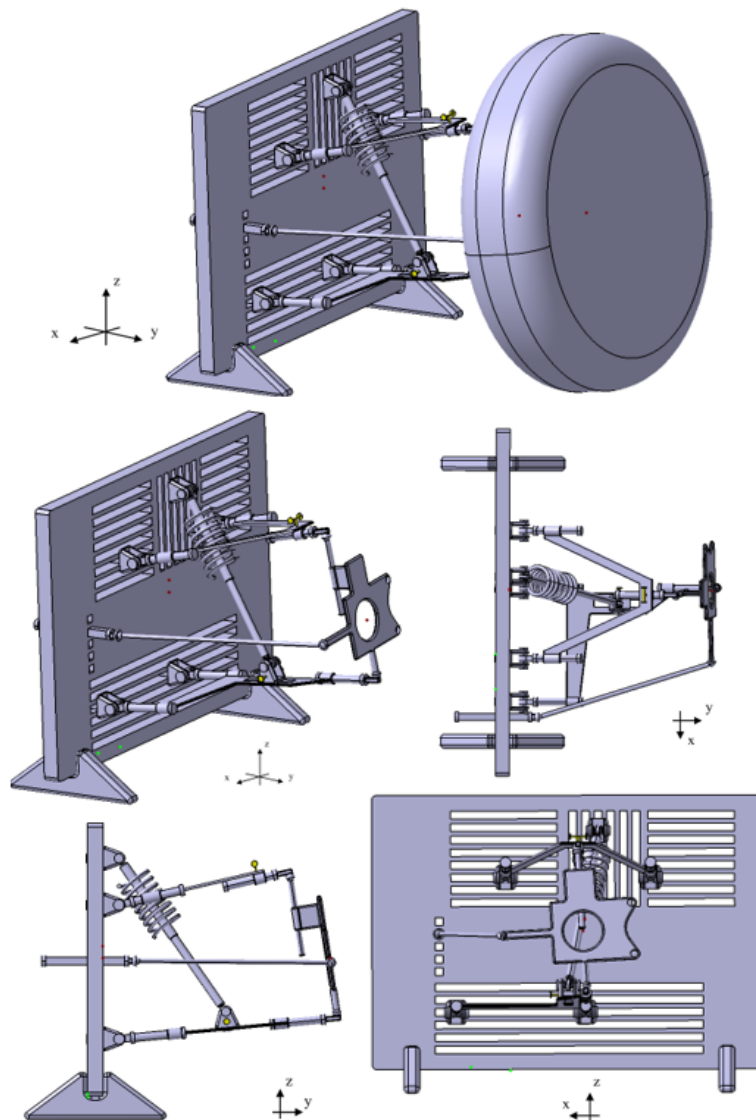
Ensamblaje de componentes del Gemelo Digital - versión Doble Trapecio.
